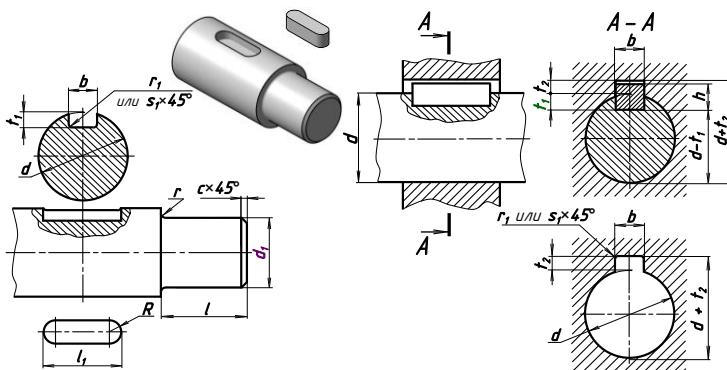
Образец формирования чертежа детали типа «Вал»
